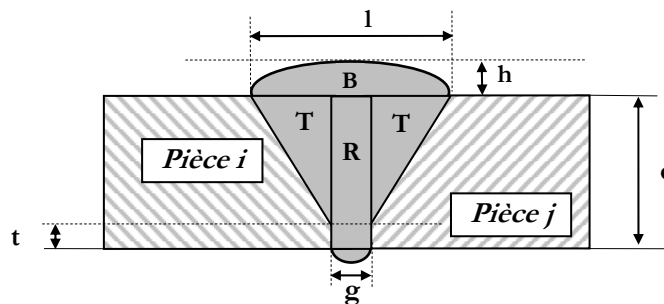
Modélisation géométrique d'une entité de soudure bout à bout en V.
